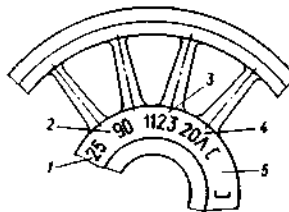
Знаки и клейма на наружном торце ступицы центра: 1 — условный номер предприятия-изготовителя; 2 — год (две последние цифры) изготовления; 3 — порядковый номер центра по системе нумерации предприятия-изготовителя; 4 — обозначение марки стали; 5 — клейма технического контроля предприятия-изготовителя и представителя заказчика
